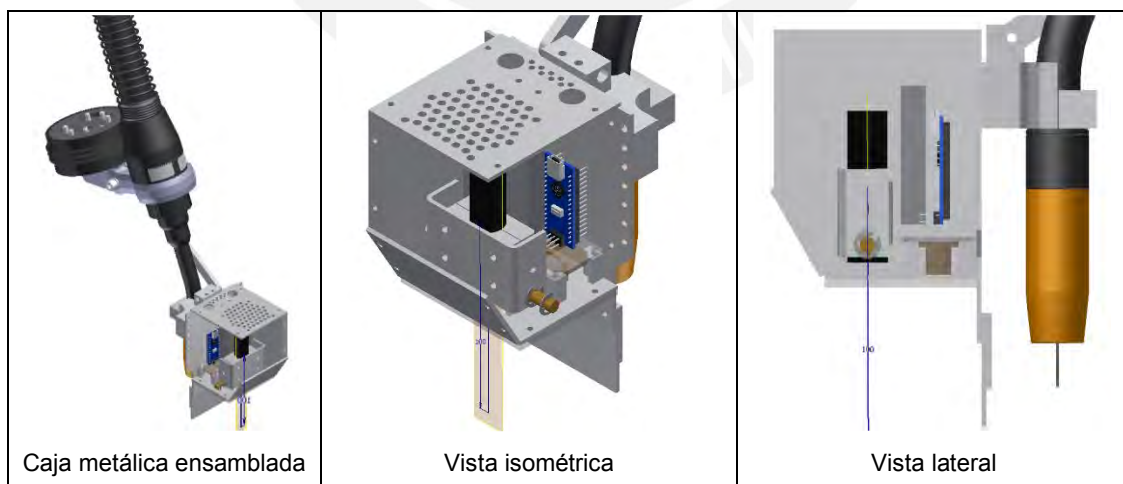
Diseño de case de sistema híbrido de sensado: caja metálica ensamblada en antorcha de soldadura (izquierda), vista isométrica de caja metálica (medio) y vista lateral de caja metálica (derecha)
